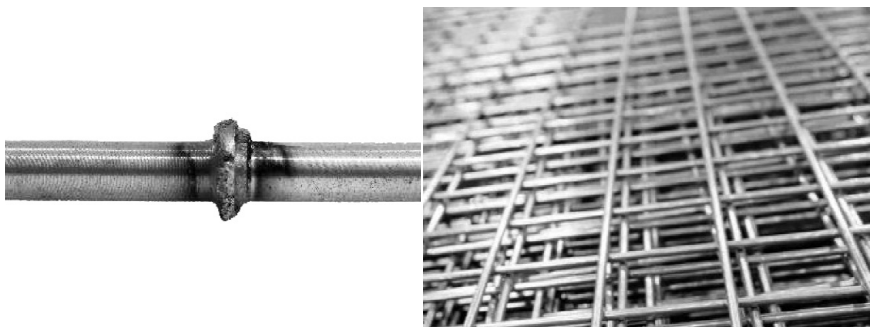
Сталевий стрижень, зварений контактним стиковим зварюванням
